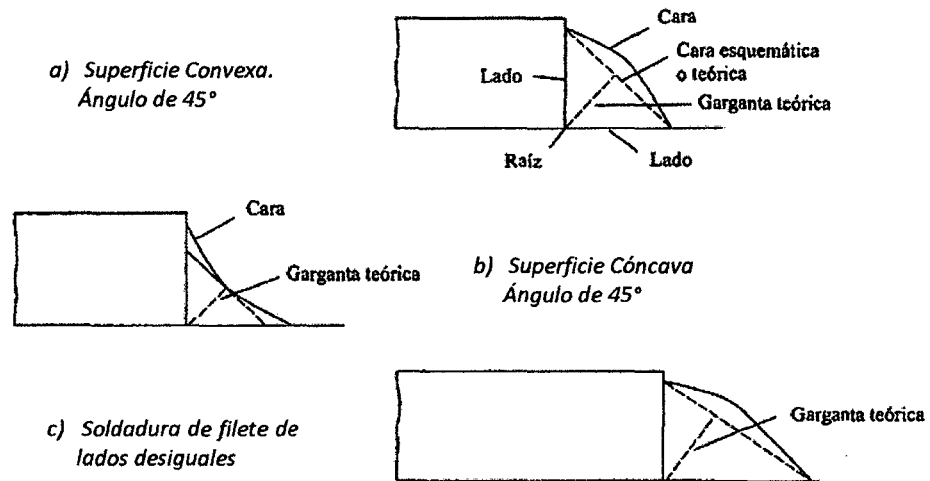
77: Tipos de Soldadura de Filete (McCormac y Csernak, 2012).
